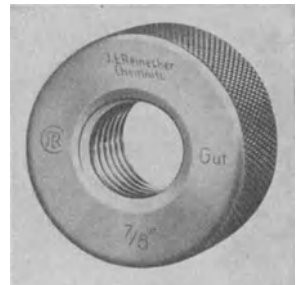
Gutgewindelehrring. (I. E. Reinecker, Chemnitz.)
